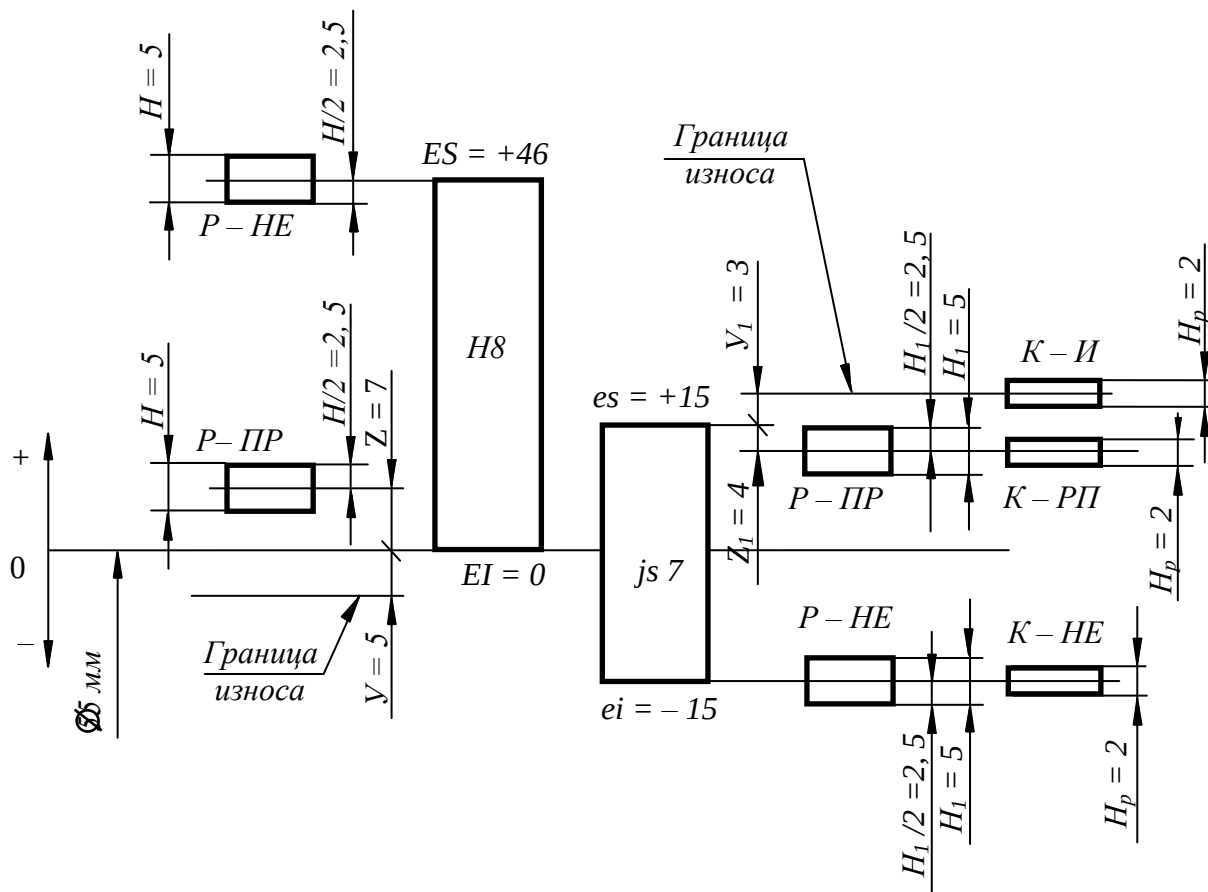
Схемы полей допусков калибров для контроля деталей соединения $\varnothing 55 H8/js7$
